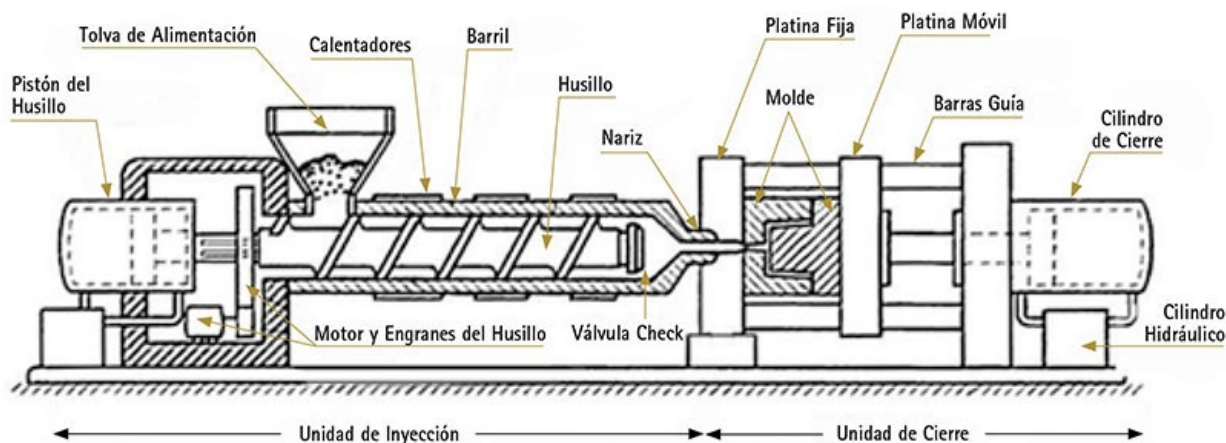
Esquema de máquina de molde de plástico por inyección.[51]
